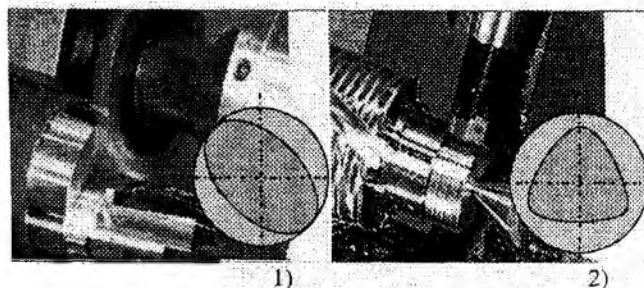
Фрезерная обработка кулачков, профиль которых представляет:
